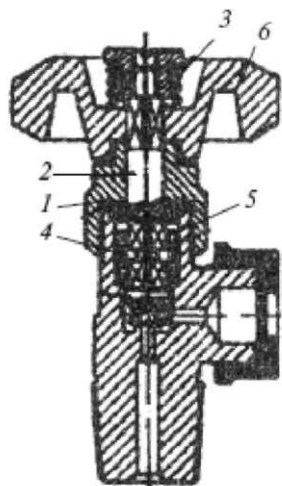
Вентиль для кислородного баллона: 1 - прокладка; 2 - шпindelь; 3 - пружина; 4 - клапан; 5 - муфта; 6 - маховичок
